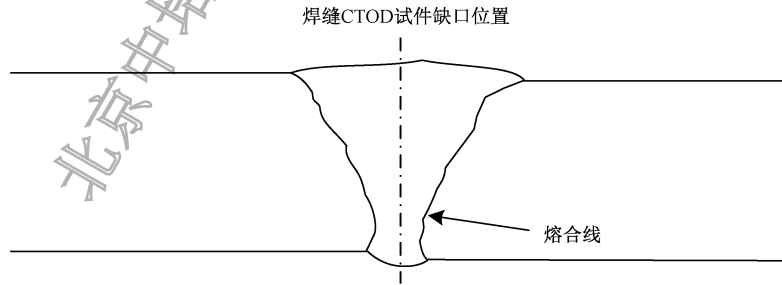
焊缝金属试样的开缺口位置示意图
